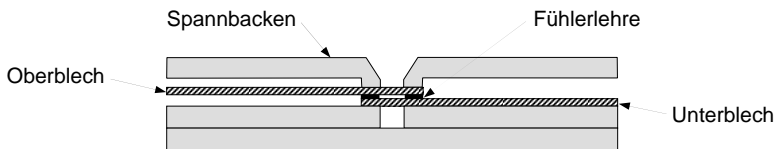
Spannvorrichtung mit eingespannten Blechen und Fühlerlehren zur Einstellung des Fügspaltmaßes.
